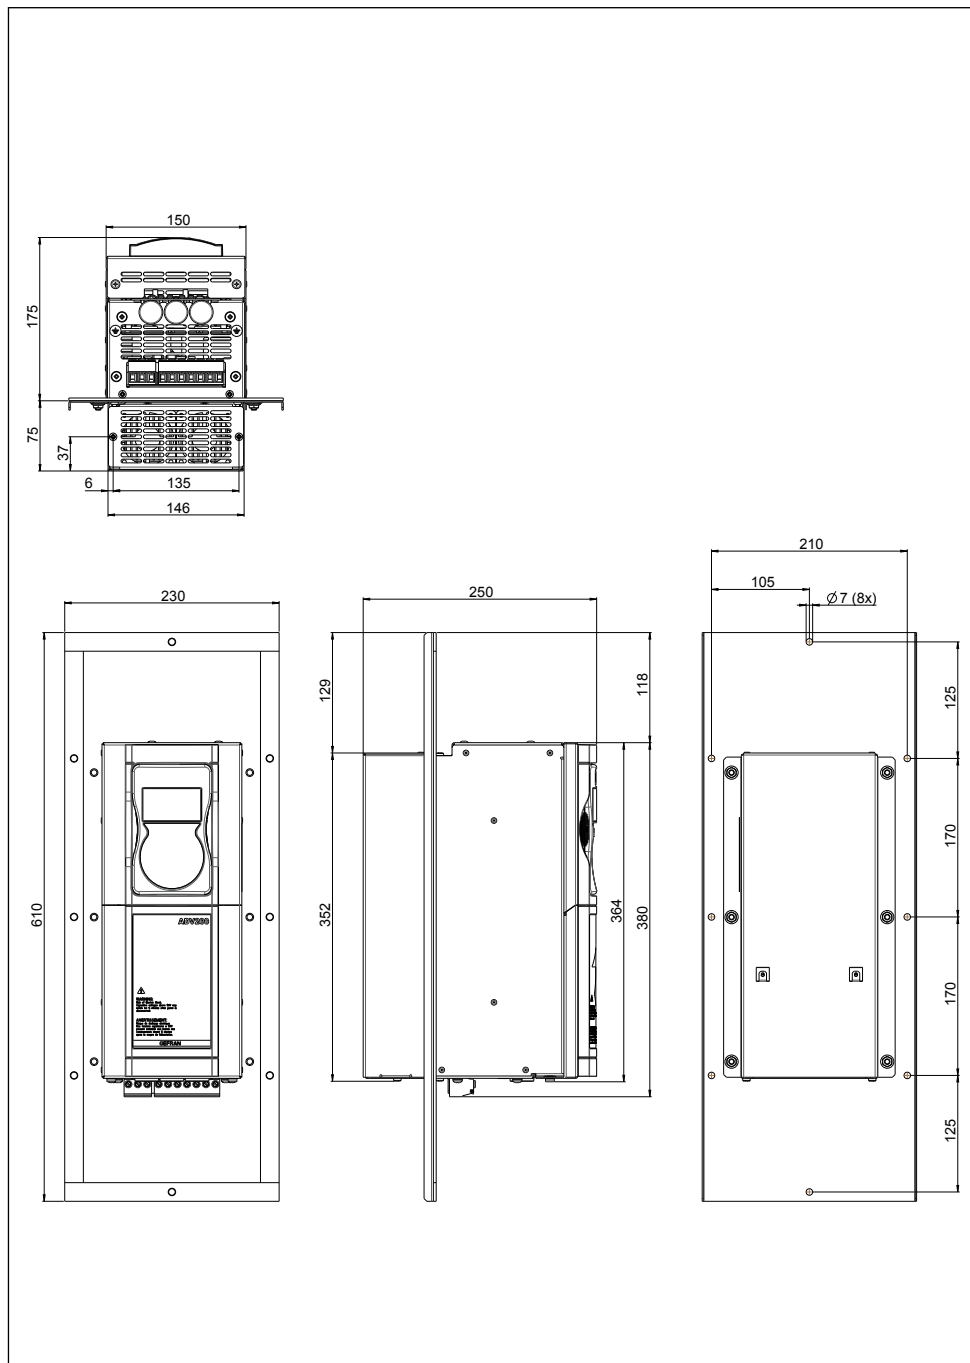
Размеры для типоразмера 3 (ADV200-...-EH)
